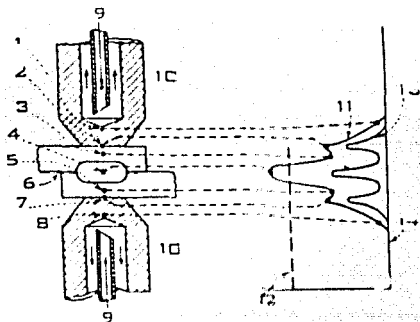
Distribución típica de la temperatura en la soldadura de punto. (Por gentileza de E. Ross, "Welding Engineering" Copyright 1954, M. C. Grass-Hill Book Co., Inc.)
